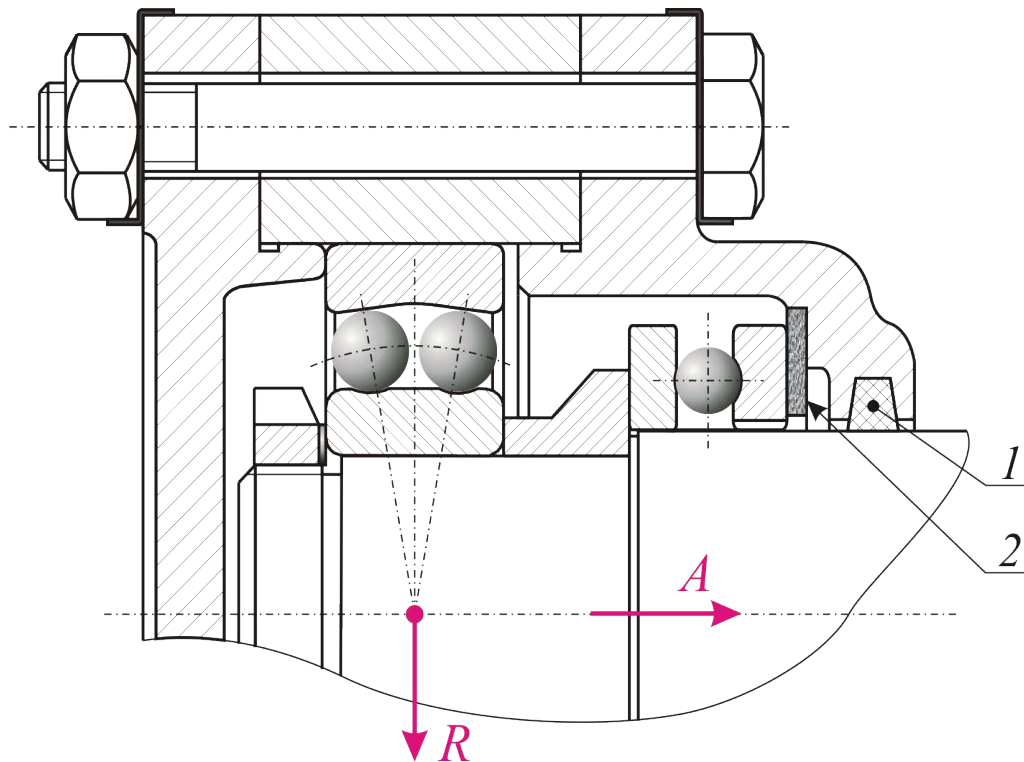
Пример установки вала на шариковых подшипниках:
